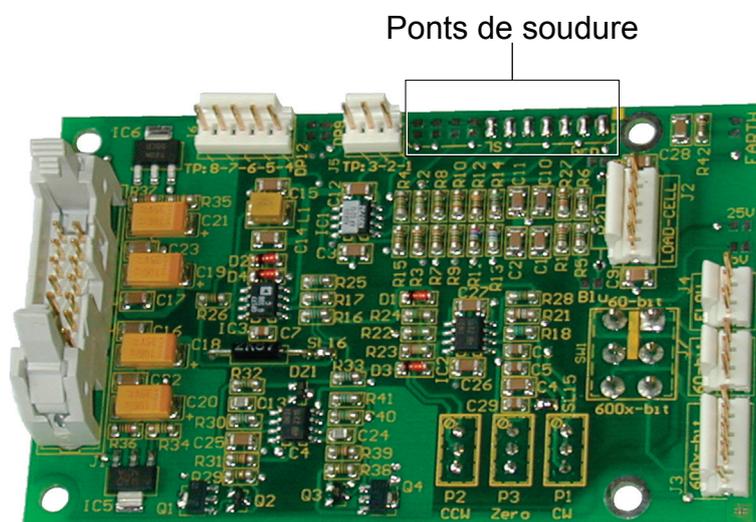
Emplacement des ponts de soudure sur le circuit imprimé du TSC 401
